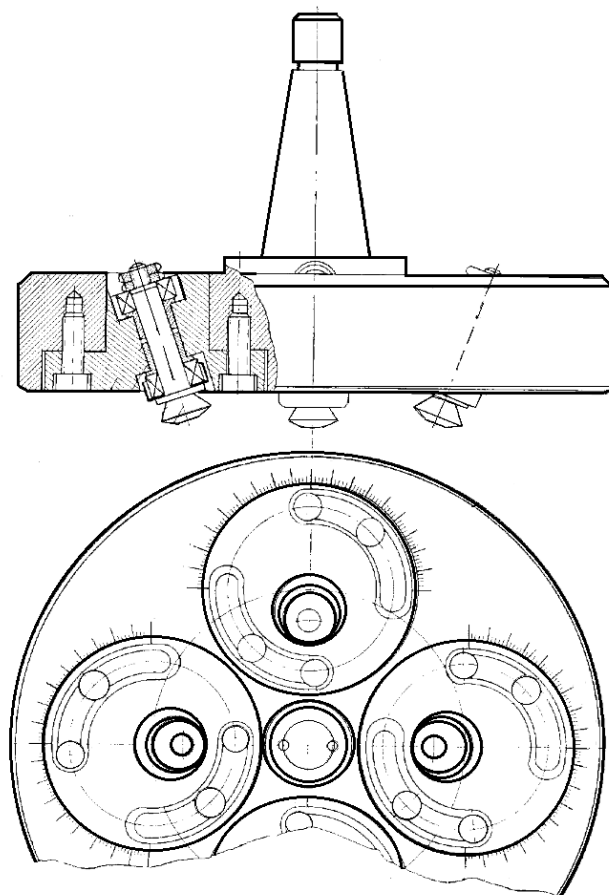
Фреза с чашечными самовращающимися резцами
